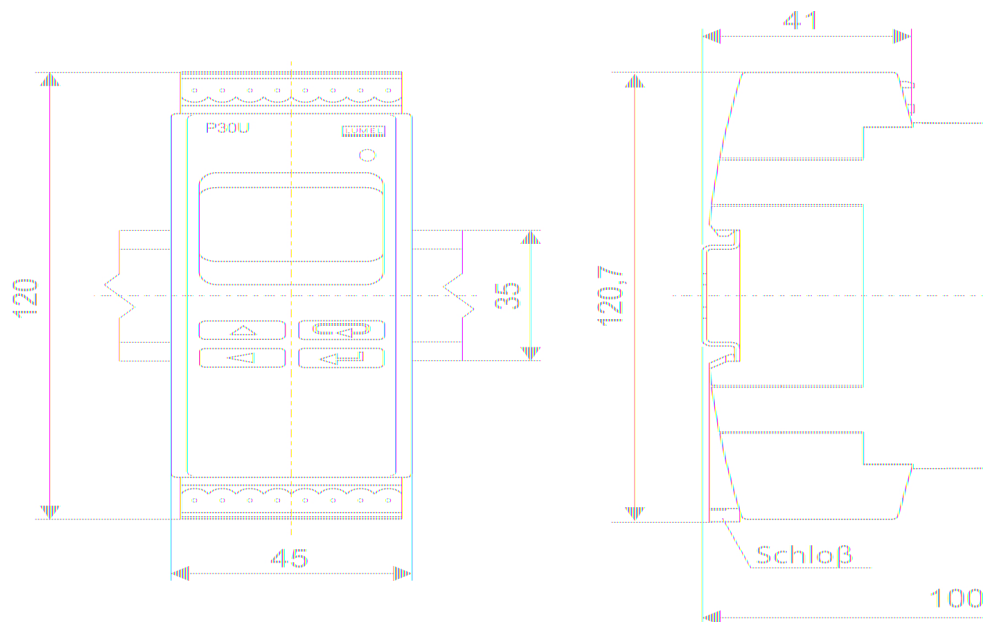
Abmessungen und Befestigungsart des Umwandlers
